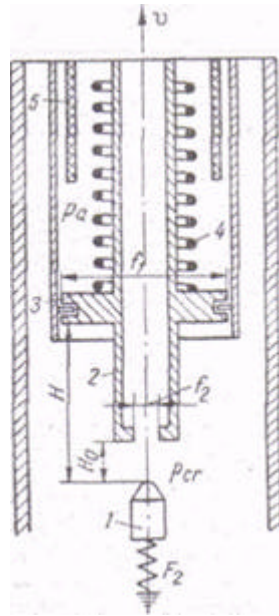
Schéma de calcul du mécanisme à contacts et piston de la chambre d'explosion de l'arc
